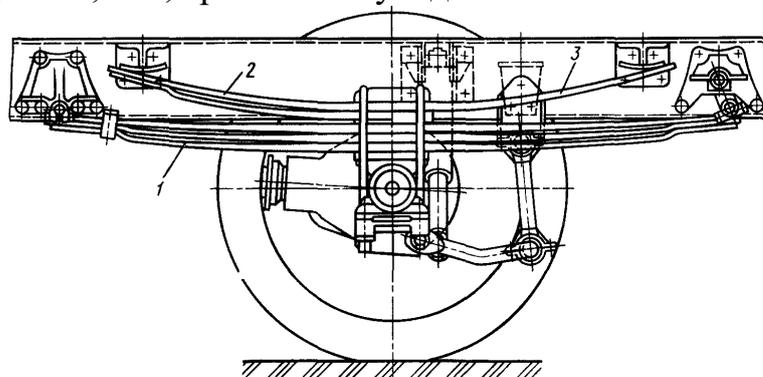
Подвеска с трехлистовой параболической рессорой щелевого типа
